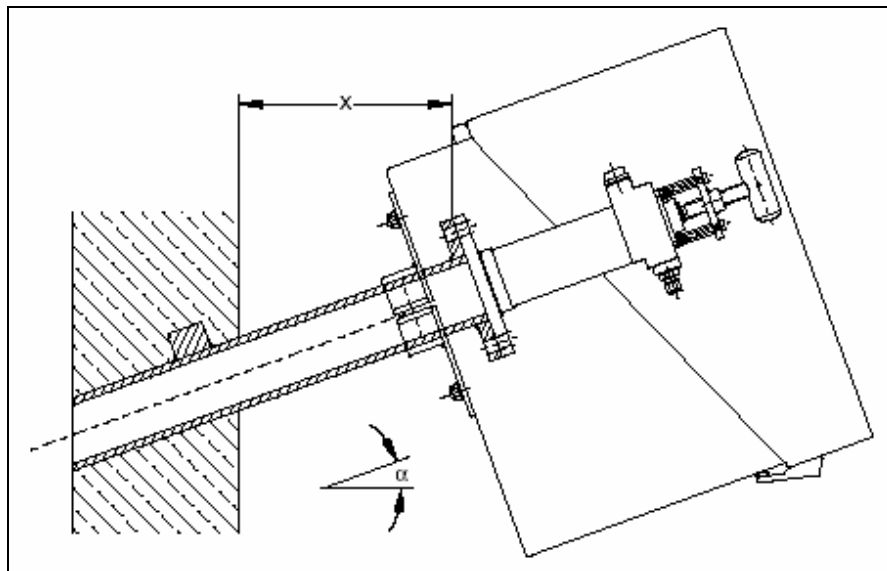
Esquema de picaje, instalación y montaje [1]
